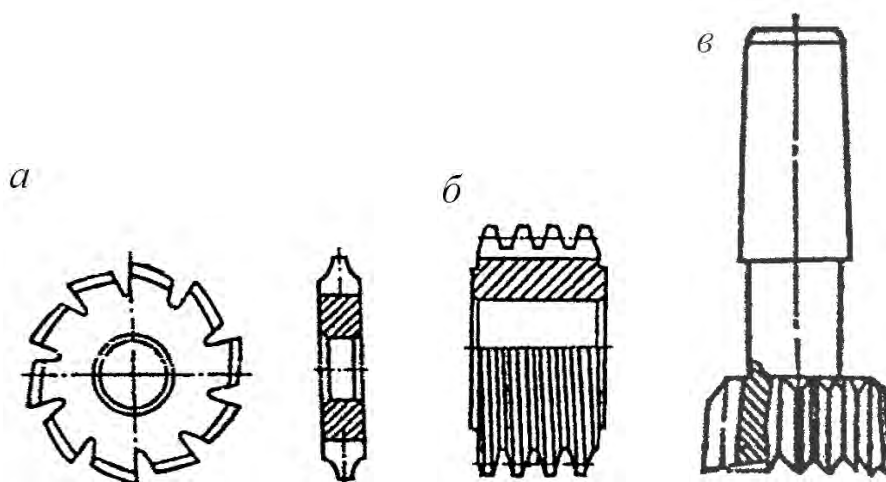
Мелкоразмерные зубонарезные инструменты
